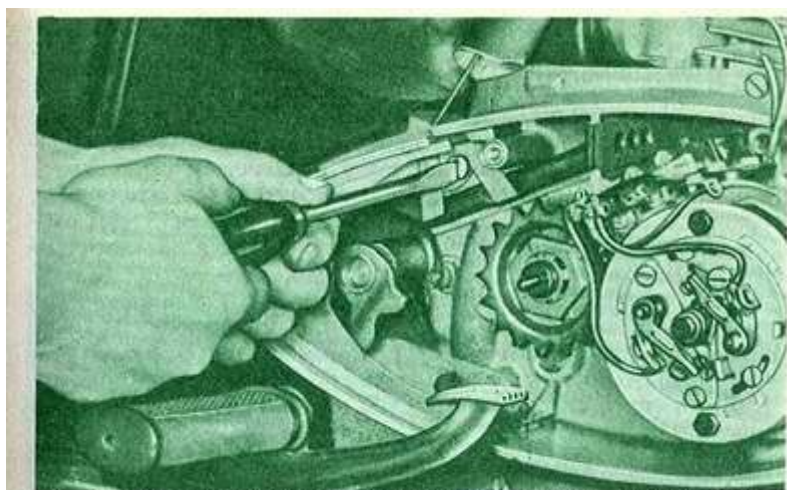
Вывертывание винта для снятия удлинителя кожуха цепи
